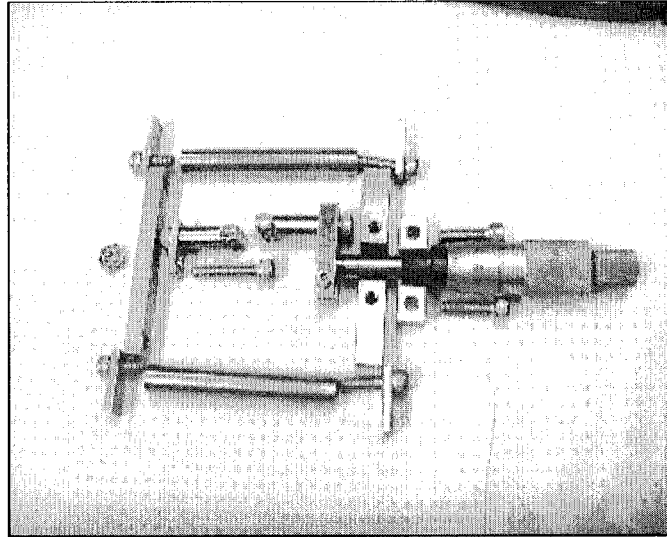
Photo des pièces du montage servant à faire les tests d'étirement sous-microscopie.
